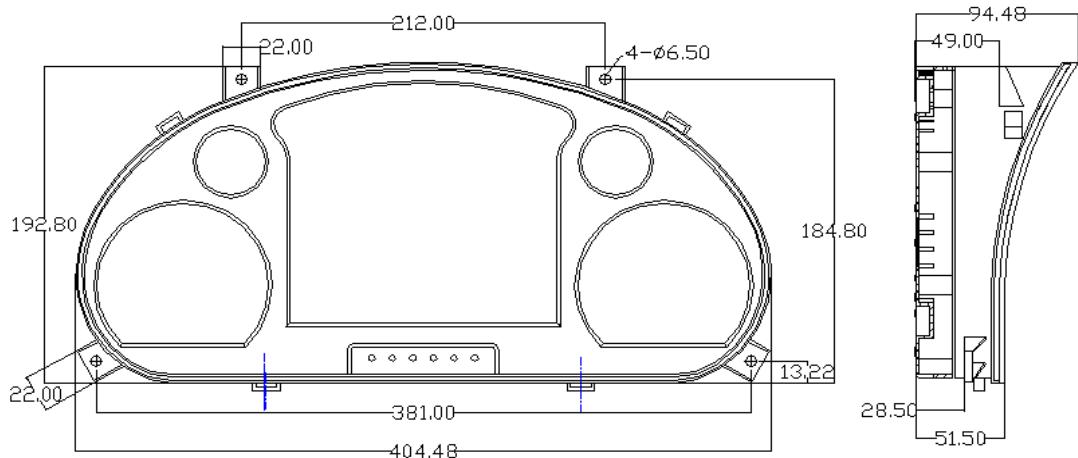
仪表安装尺寸/Fig.6-4-1 Installing Dimension of Dashboard
